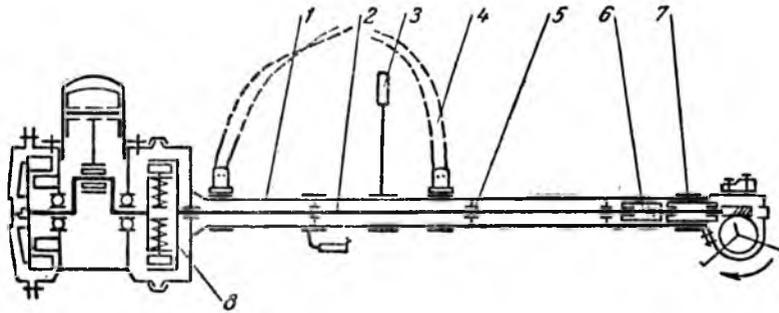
Кинематическая схема мотоагрегата РА-1: 1 — кожух, 2 — приводной вал, 3 — рукоятка, 4 — ремень, 5 — подшипник, 6 — шлицевая муфта, 7 — хомут, 8 — полу муфта автоматического центробежного сцепления.
